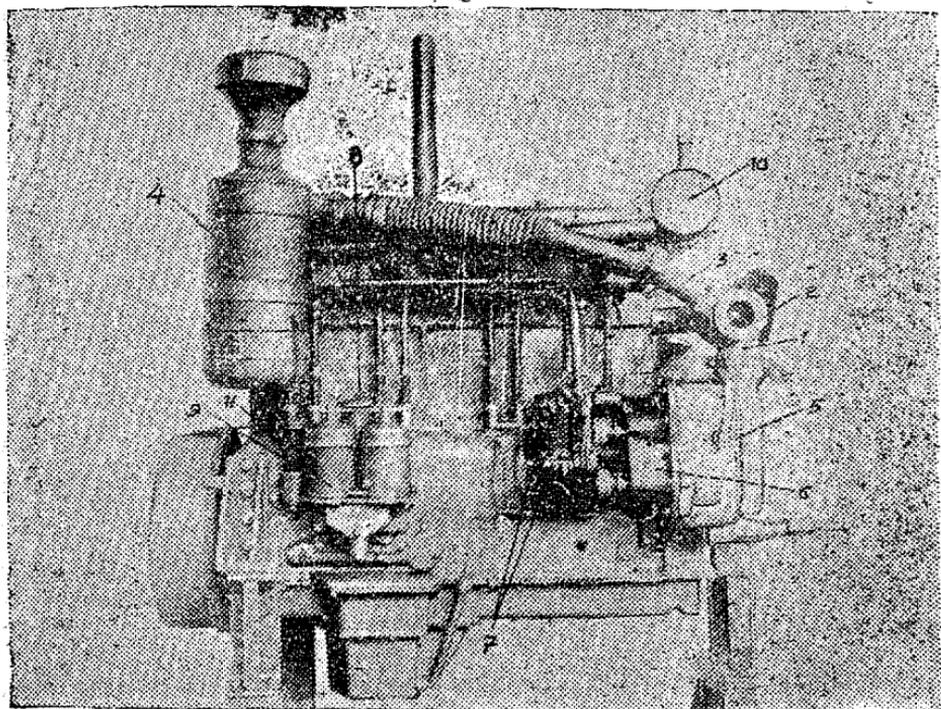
Общий вид газового двигателя МГ—17 справа: 1—корпус дроссельной заслонки; 2—смеситель; 3—патрубок подвода воздуха к смесителю; 4—воздухоочиститель; 5—кожух шестерен распределения; 6—кронштейн магнето; 7—магнето; 8—маслоналивная горловина; 9—масляные фильтры; 10—бензиновый бачек пускового двигателя; 11—свечи.
